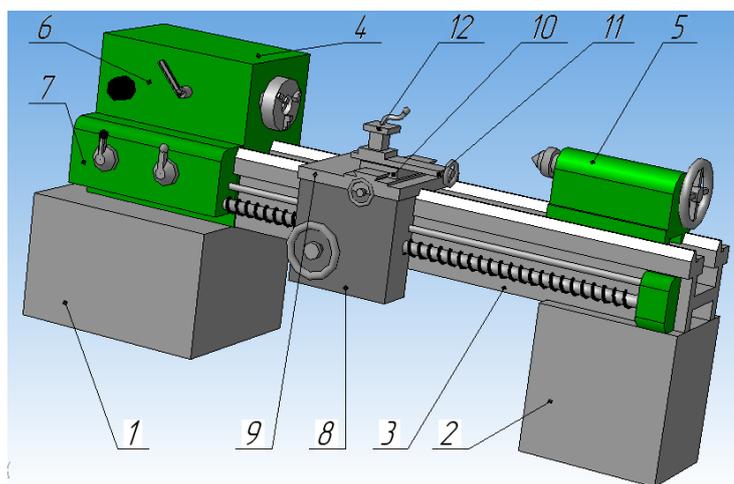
Устройство токарно-винторезного станка 16К20
